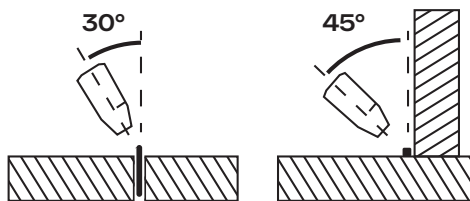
Положение сопла горелки при сварке, угол В
